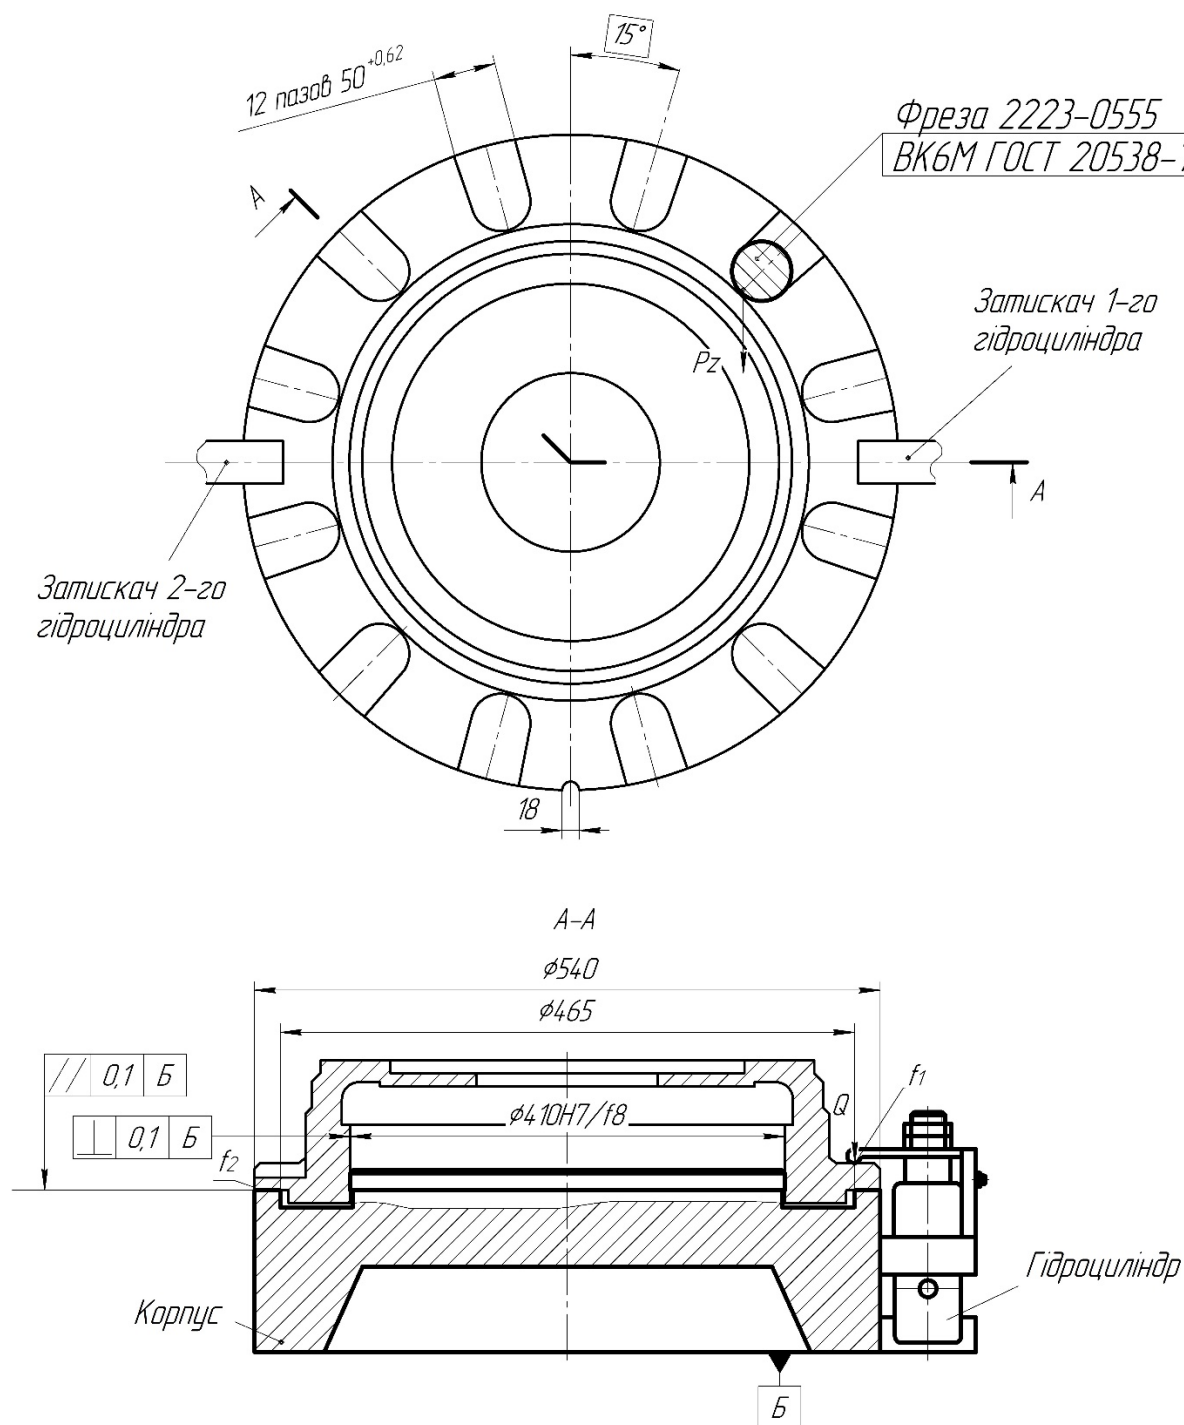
Схема для розрахунку сили закріплення заготовки
